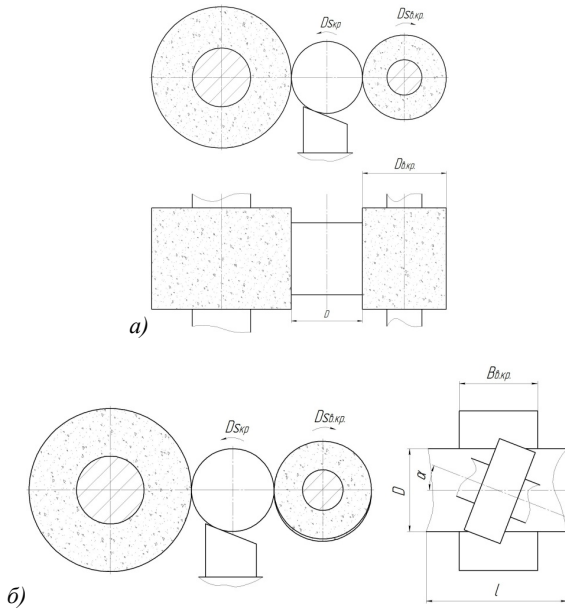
Круглое наружное бесцентровое шлифование:
